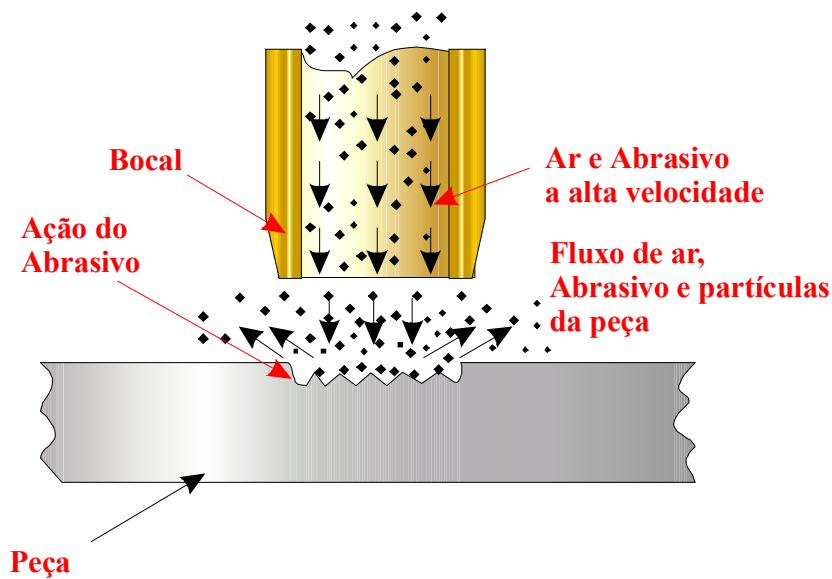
Princípio da Usinagem por Jato Abrasivo (Tuersley et al, 1994).
